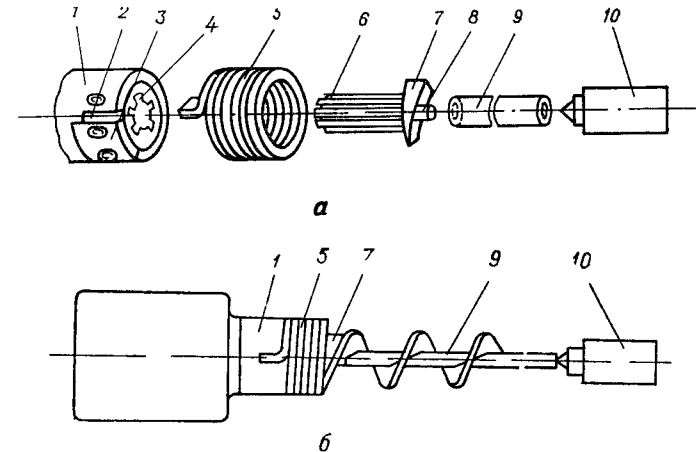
Схема приспособления для калибровки спиралей по шагу (а) и технологический процесс калибровки спирали по шагу (б).
